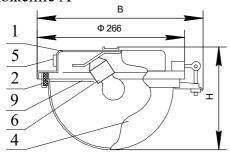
ФПП03-...-001 1.Корпус в сборе; 2.Кольцо в сборе; 4.Рассеиватель; 5.Садьниковый ввод или заглушка; 6.Патрон; 9.Экран.
